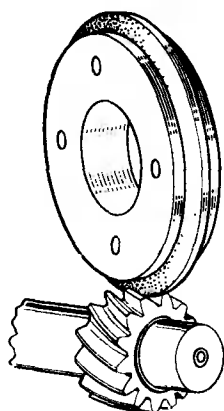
Схема шлифования зубчатого колеса профильным эльборовым кругом
